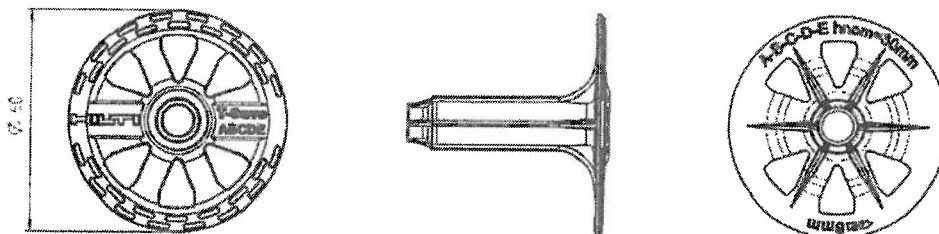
T-Save HTS-M - zamontowana tuleja, talerzyk dociskowy i gwóźdź kompozytowy
